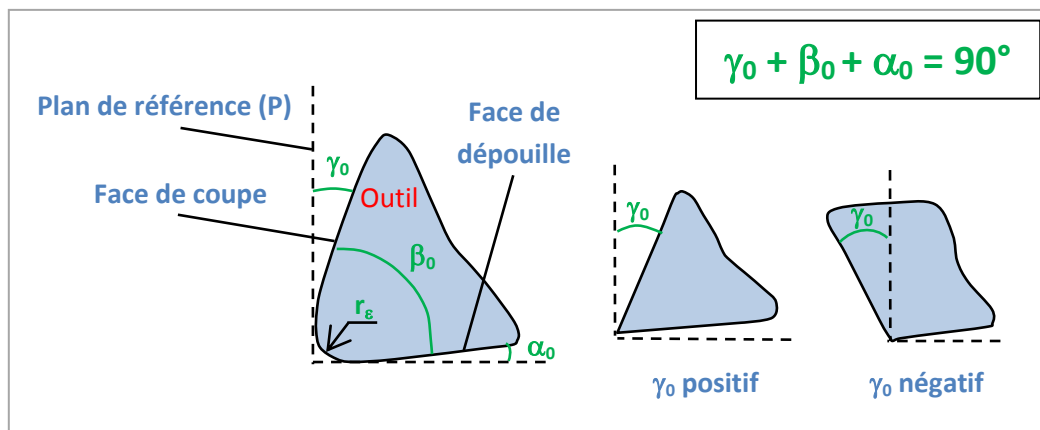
Angles de coupe d'un outil en travail [VEL07]
